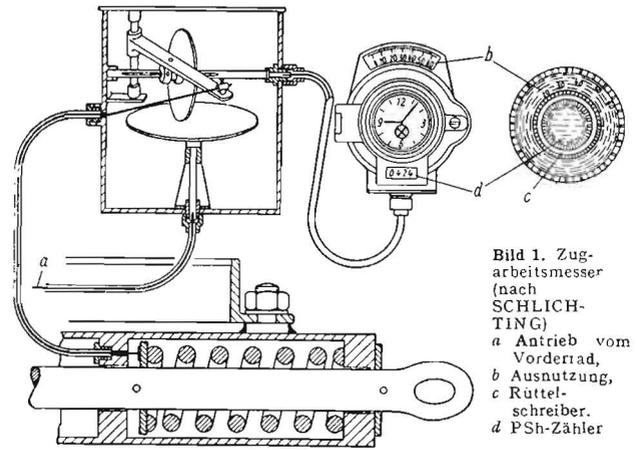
Zugkraftmessers (nach SCHLICHTING)
